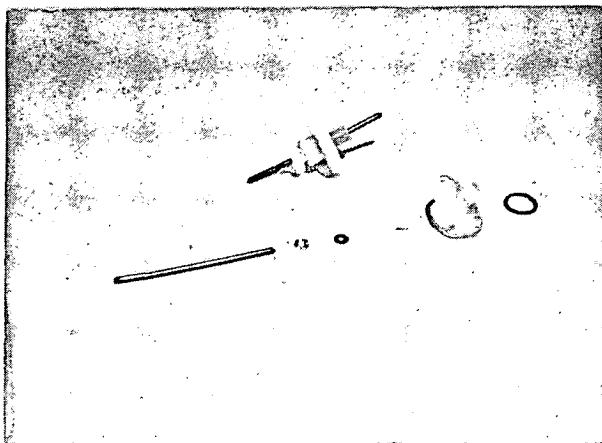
Vista do passante montado e do conjunto de partes que o constituem.
